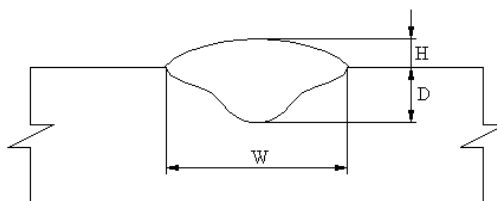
Representação esquemática da soldagem “bead on plate”: Largura do cordão (W), Profundidade do cordão (D) e Reforço do cordão (H).
